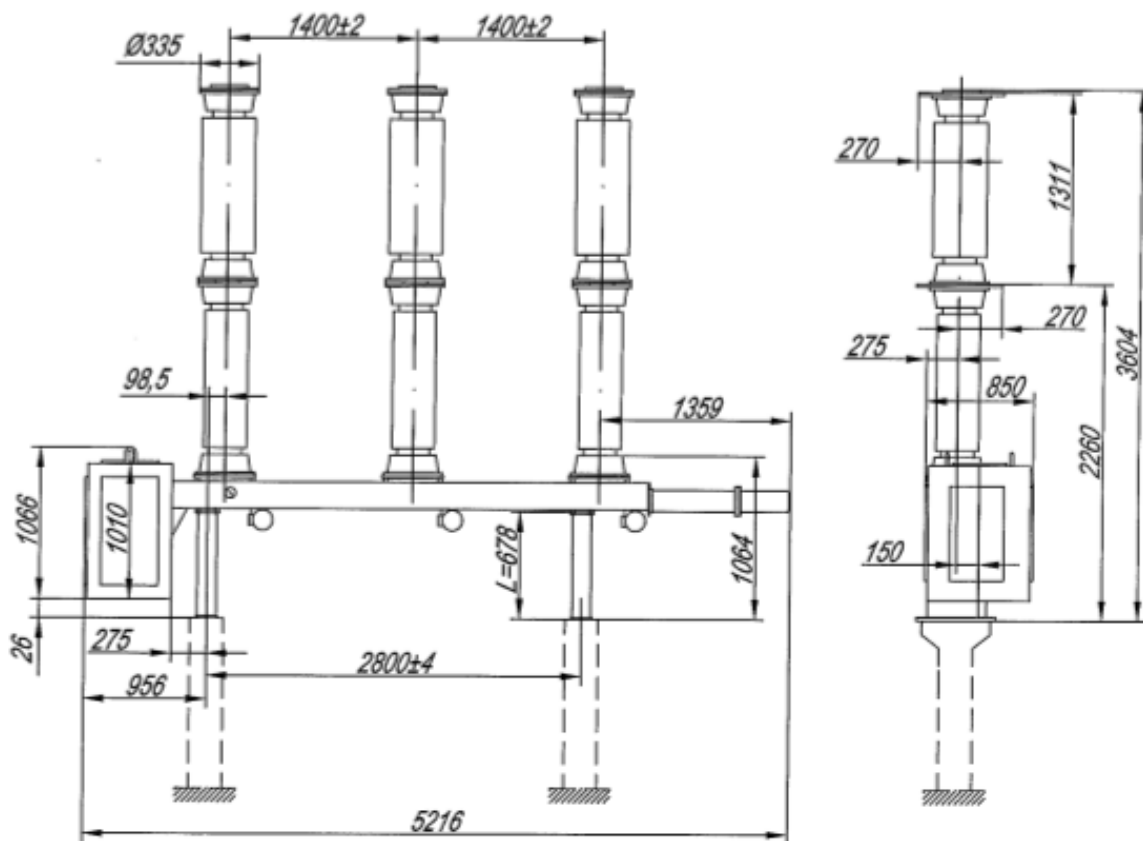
Габаритные размеры выключателя ВГТ-110
